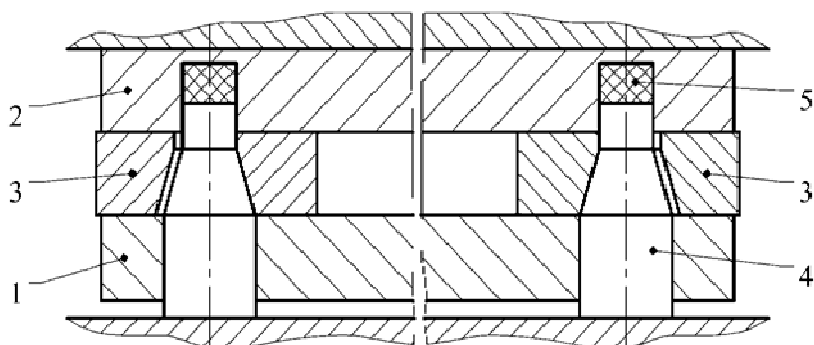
Пресс-форма для формования вставок пантографов: 1, 2 – боковины; 3 – торцевые пластины; 4 – соединительный штифт; 5 – упругий элемент
